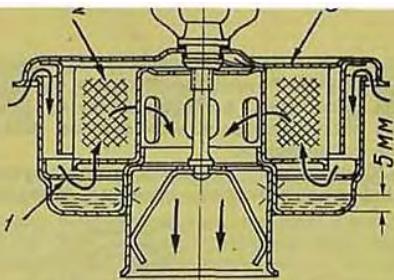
Фильтр открытой вентиляции: 1 — корпус фильтра; 2 — фильтрующий элемент (картоновая сетка); 3 — крышка фильтра.
